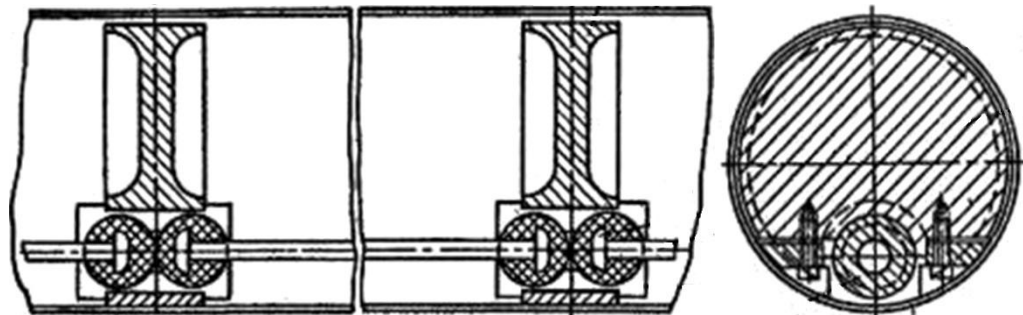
трубчатий шарнірний скребокний конвеєр
